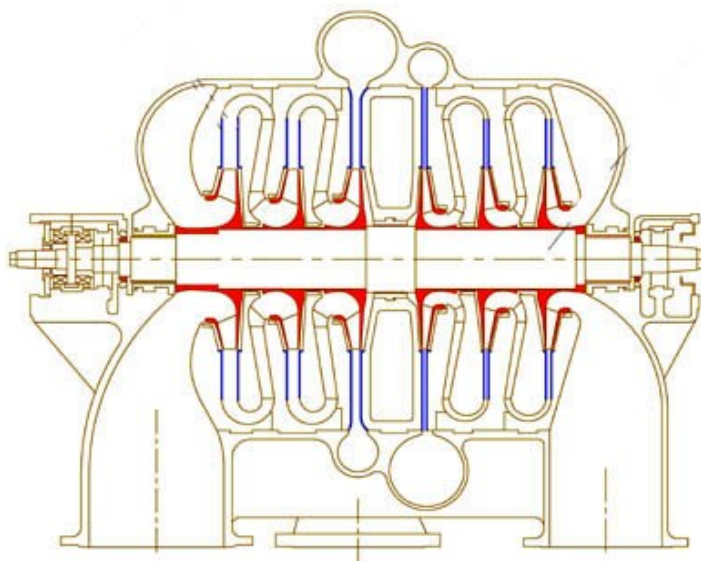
Продольный разрез ЦВД модернизированного компрессора
